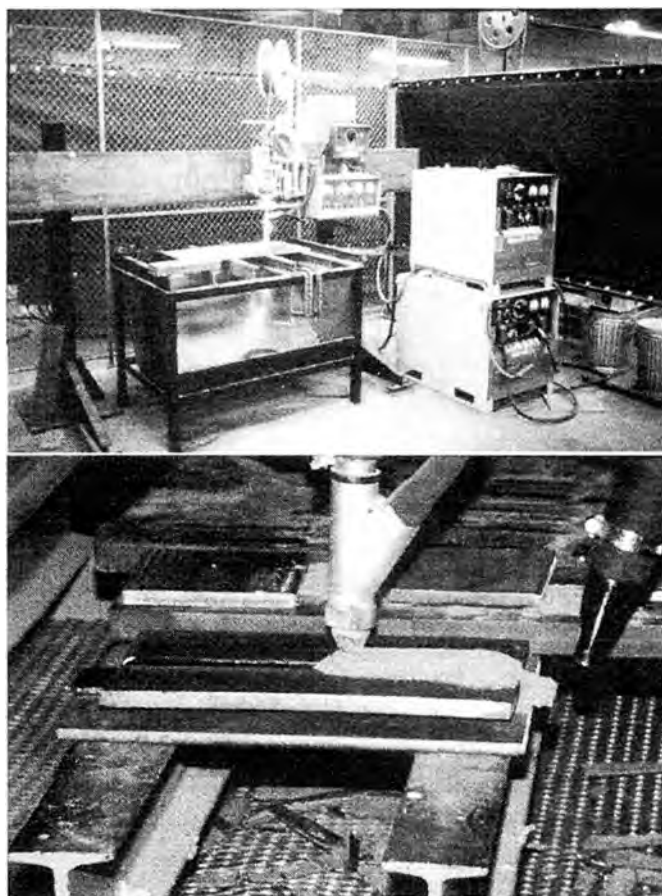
Equipo de Soldadura por Arco Sumergido
